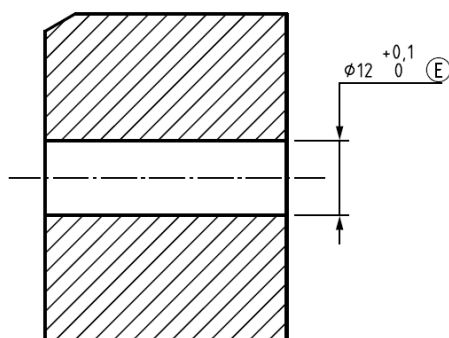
Značka modifikátoru pro rozměr ze dvou bodů [5]
